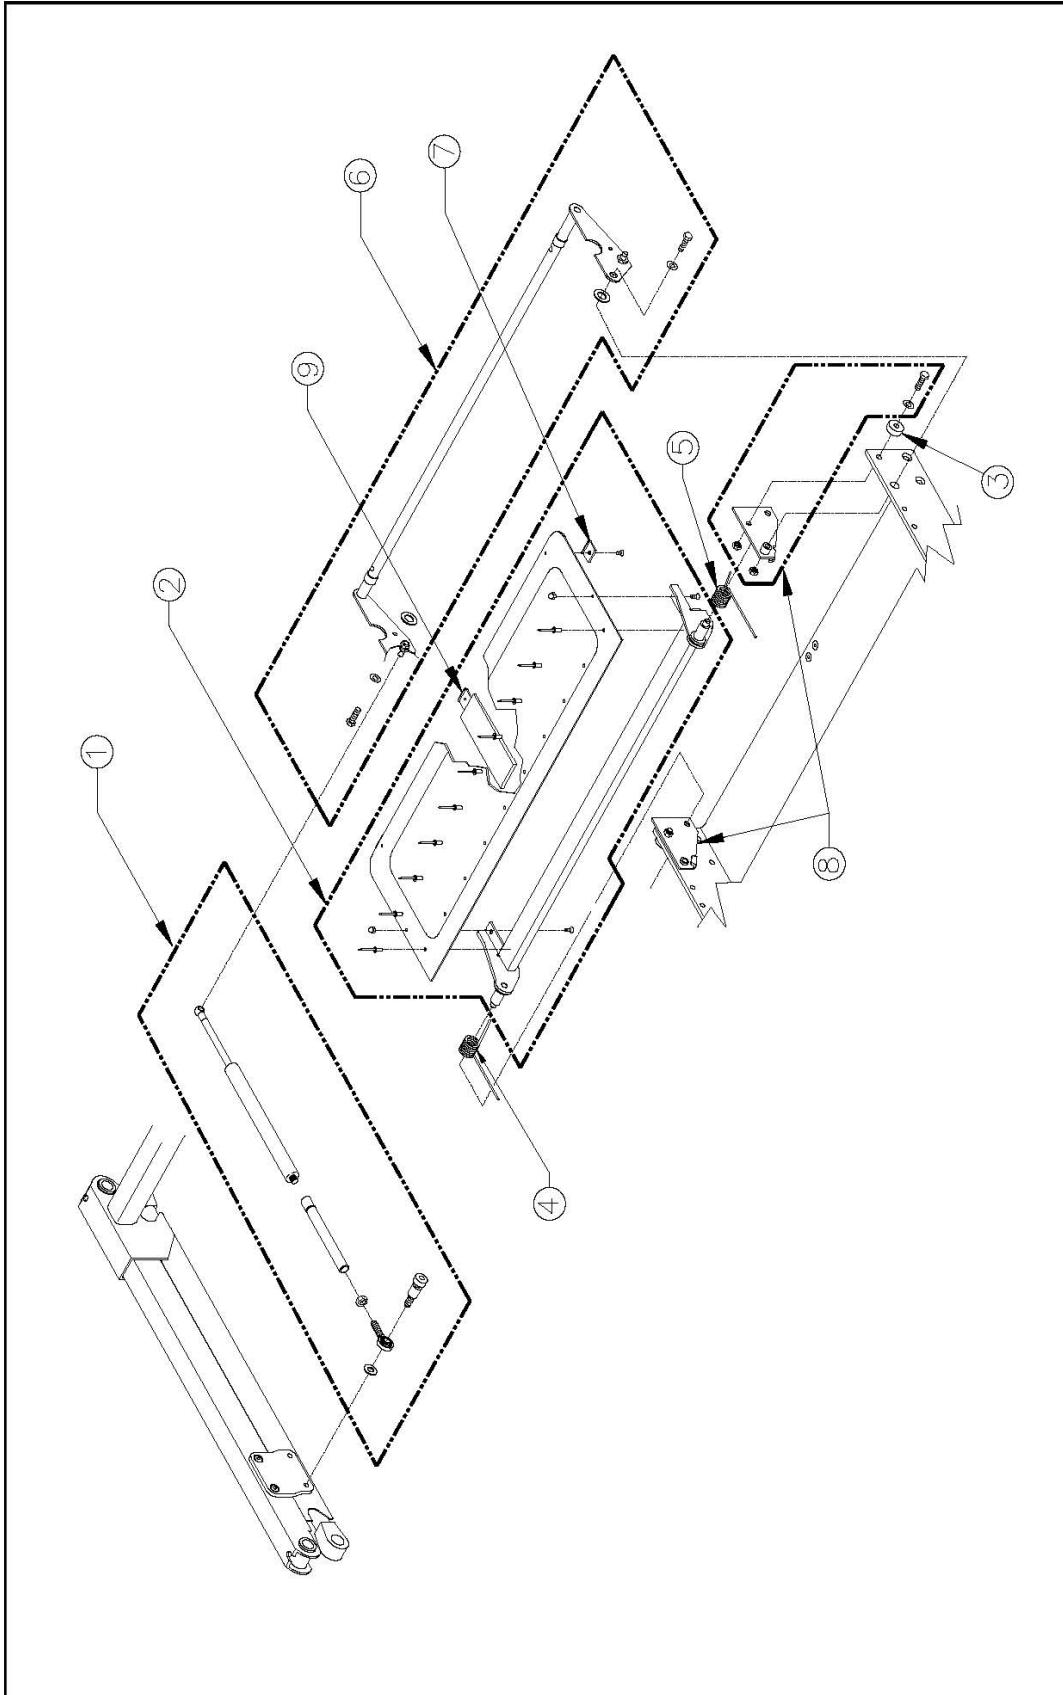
SPONDA DI COLLEGAMENTO DELL'F9T – PORTA RISERVATA
